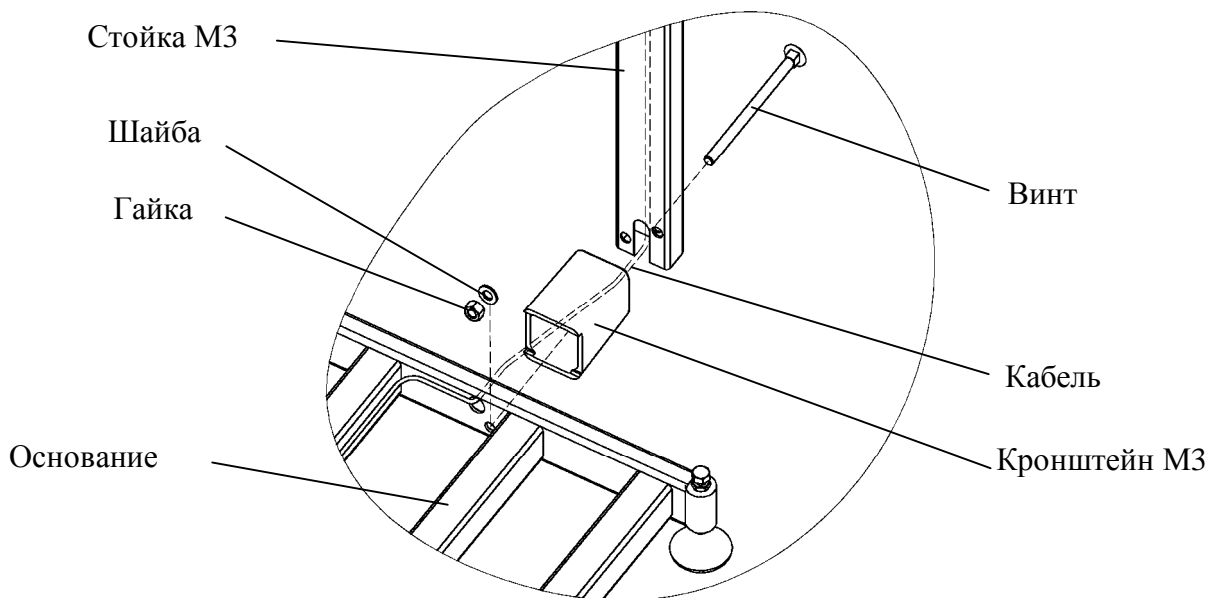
Крепление прямоугольной стойки к основанию весовой платформы ТВ-М\
